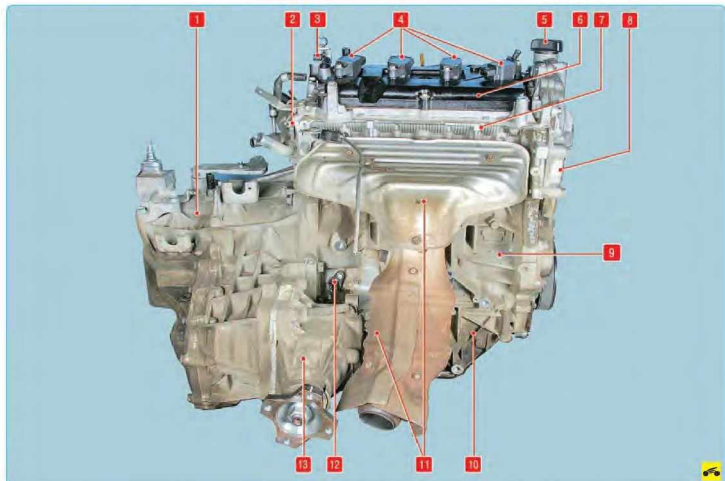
Силовой агрегат с двигателем объемом 2,0 л и механической коробкой передач (вид сверху, впускной коллектор снят): 1 – коробка передач; 2 – корпус распределителя охлаждающей жидкости; 3 – датчик положения впускного распределительного вала; 4 – катушки зажигания; 5 – пробка масляной ванны горловины; 6 – крышка головки блока цилиндров; 7 – головка блока цилиндров; 8 – крышка газораспределительного механизма; 9 – блок цилиндров; 10 – масляный картер двигателя; 11 – термозащиты катколлектора; 12 – датчик положения коленчатого вала; 13 – раздаточная коробка
